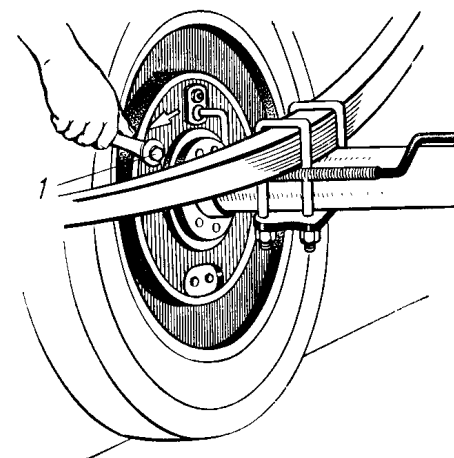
Регулировка зазора между колодкой и тормозным барабаном заднего колеса:
